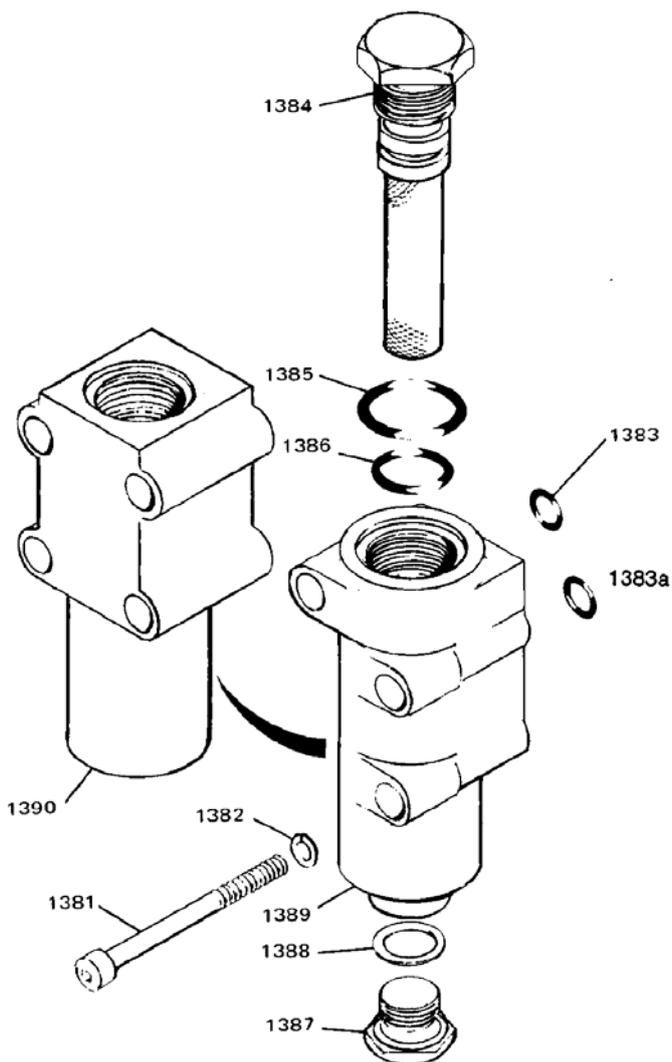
Explosionsdarstellung des Filters für aufladedruckabhängige Füllungsbegrenzer
